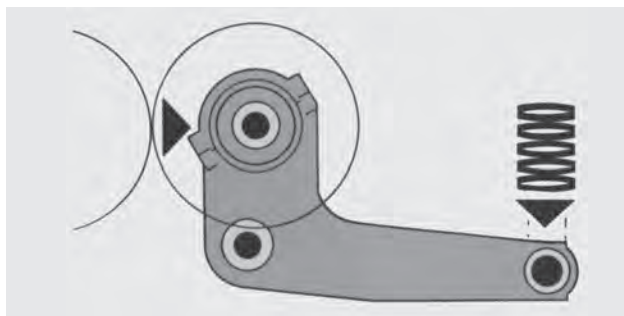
Gegen Tellerfederpakete abgestützte Schwinge
